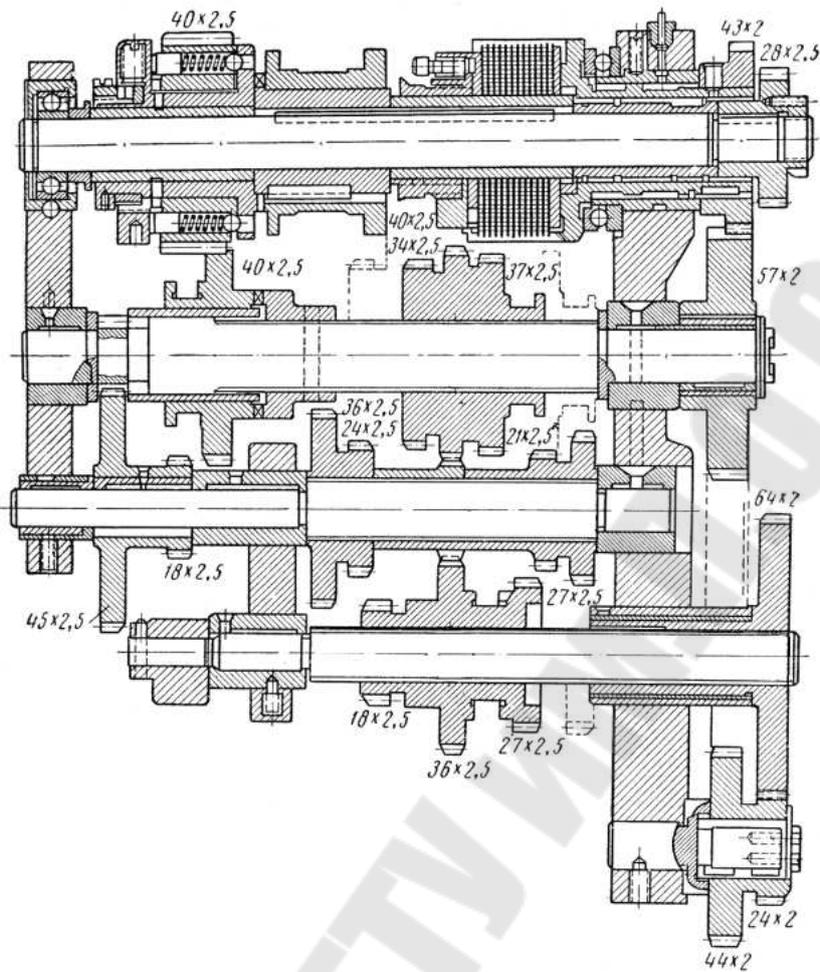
Коробка подачи горизонтально-фрезерного станка 6Н82
